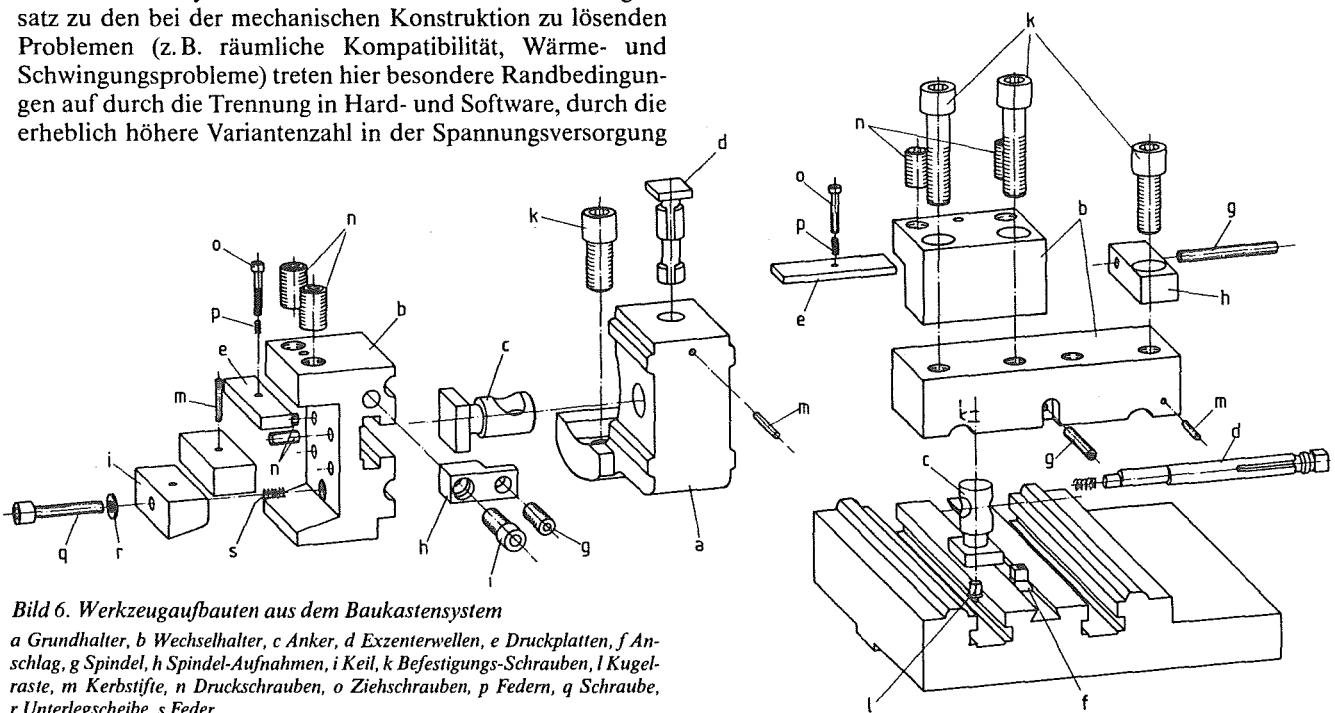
Werkzeugaufbauten aus dem Baukastensystem
